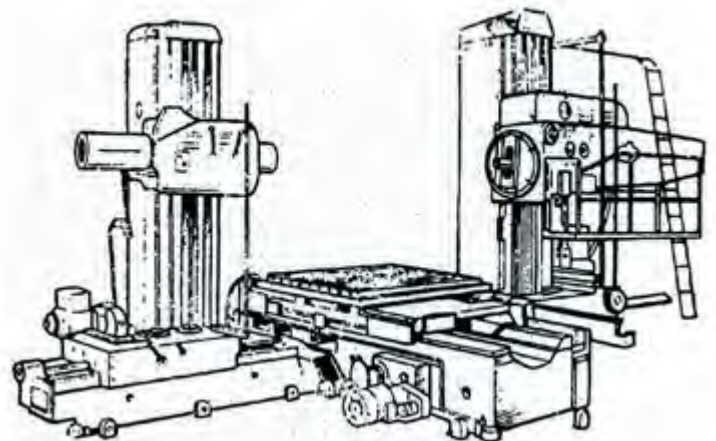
Горизонтально-розточувальний верстат (мод. 2654)
